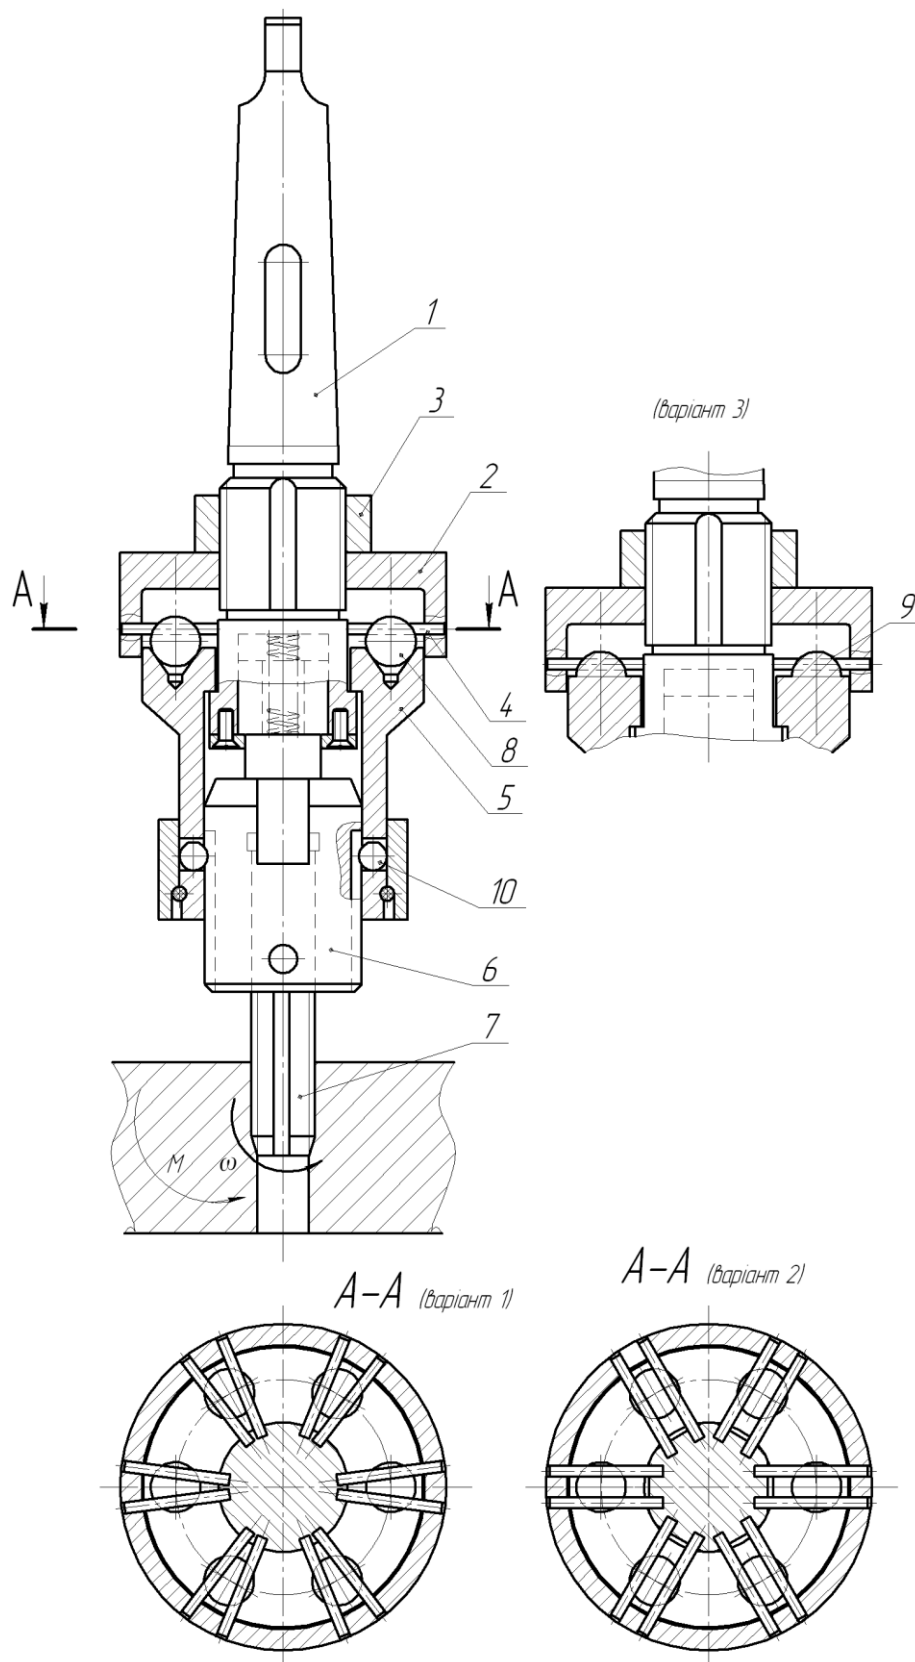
Конструктивна схема запобіжного патрона для осьових інструментів
